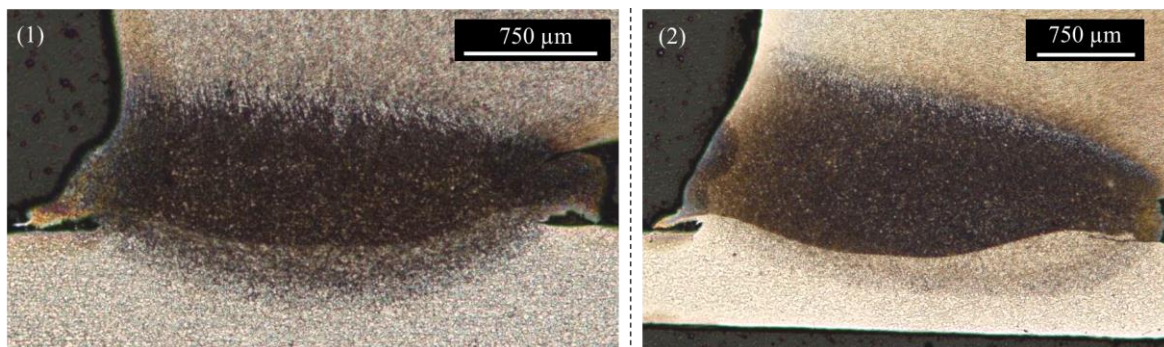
Lokale Geometrie der Schweißnaht der Mutterprobe, rund geschweißt 210-16 (1) und 3 Segmente geschweißt 210-08 (2)
